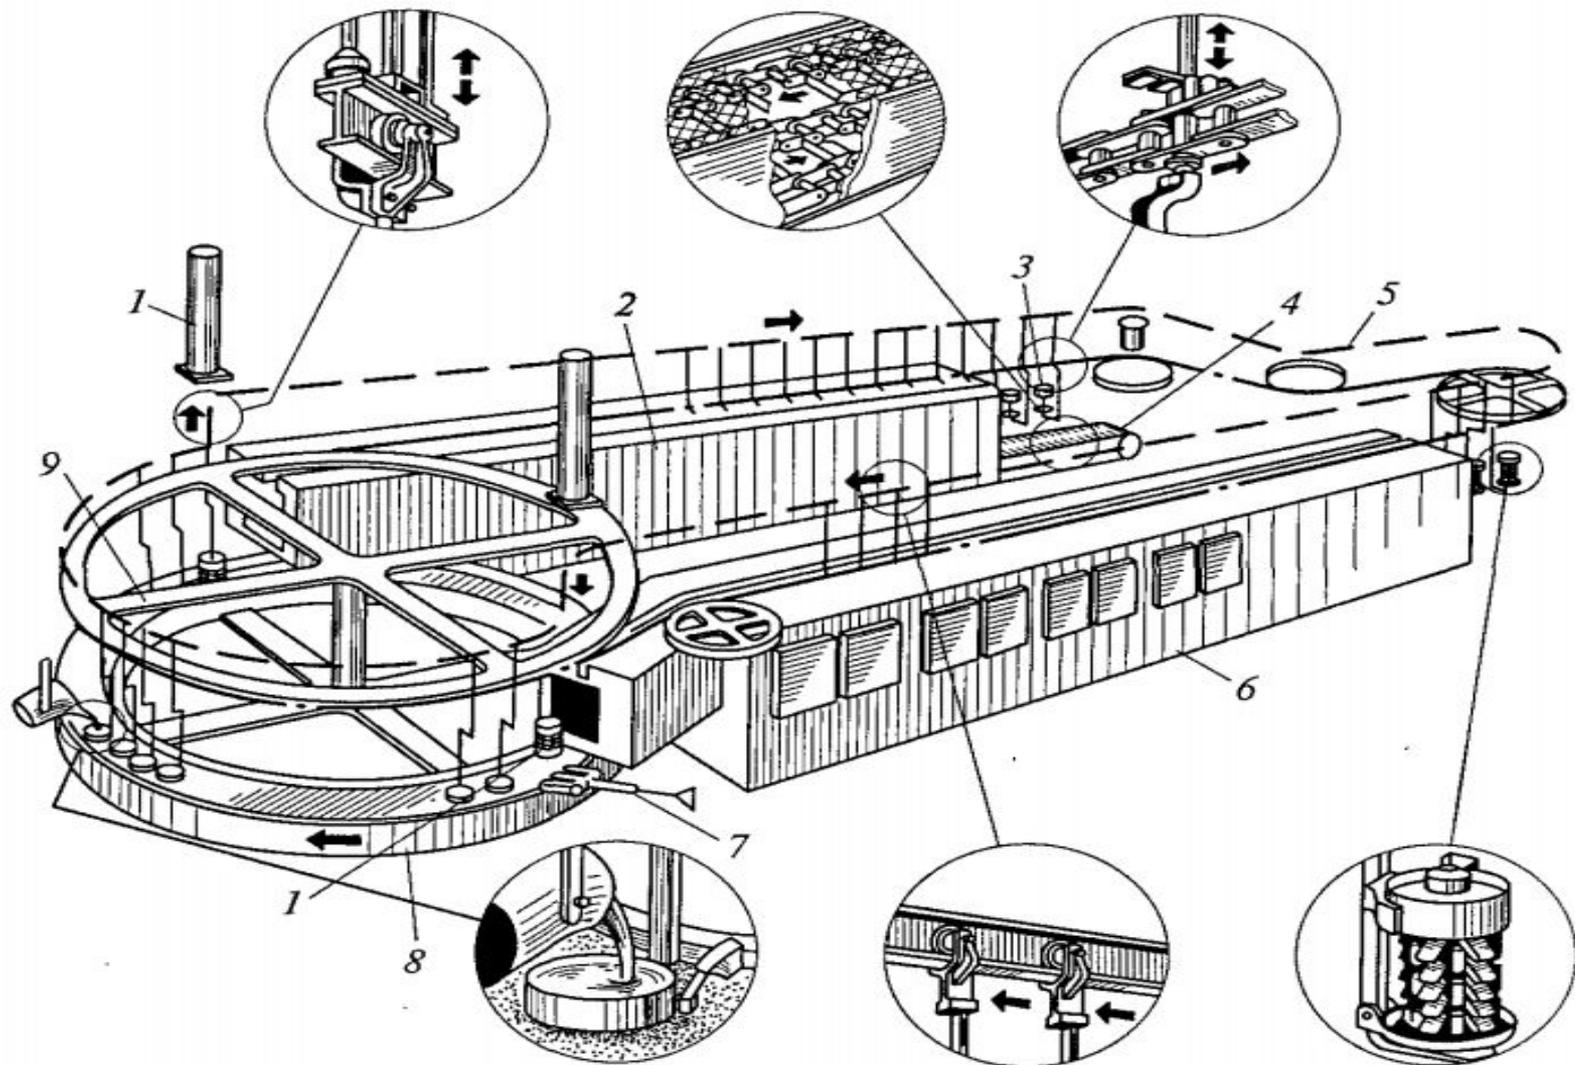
Схема агрегата для прокаливания, формовки, заливки и выбивки оболочковых форм:
